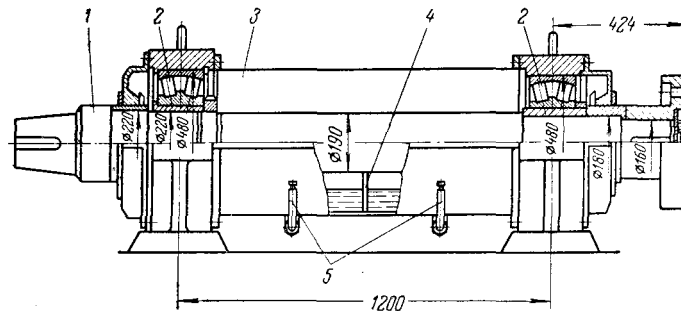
Вал вентилятора ВЦ-25 и ВЦ-11
